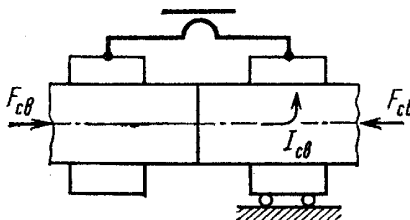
Схема стыковой контактной сварки.
